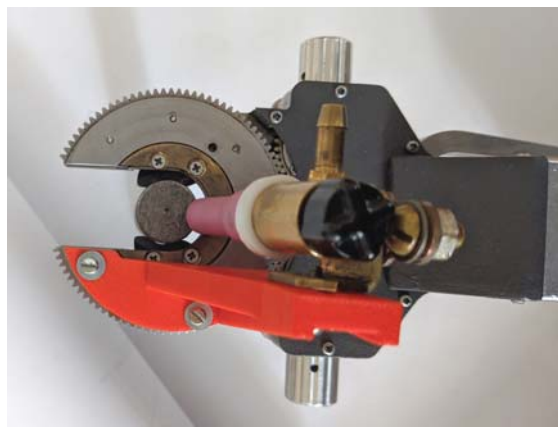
Установленный кронштейн на орбитальную сварочную головку
